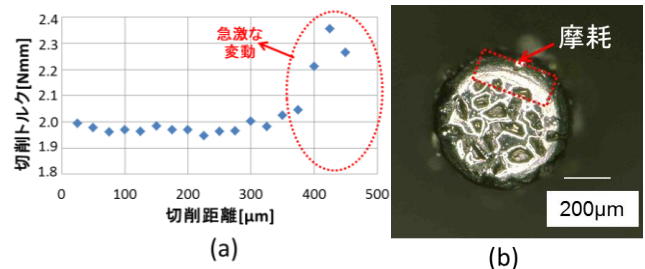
(a)推定切削トルク (b)切削距離 325 μm 後の
